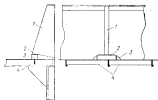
Варианты конструкции соединяющего крепления фальшбортовой стойки:
